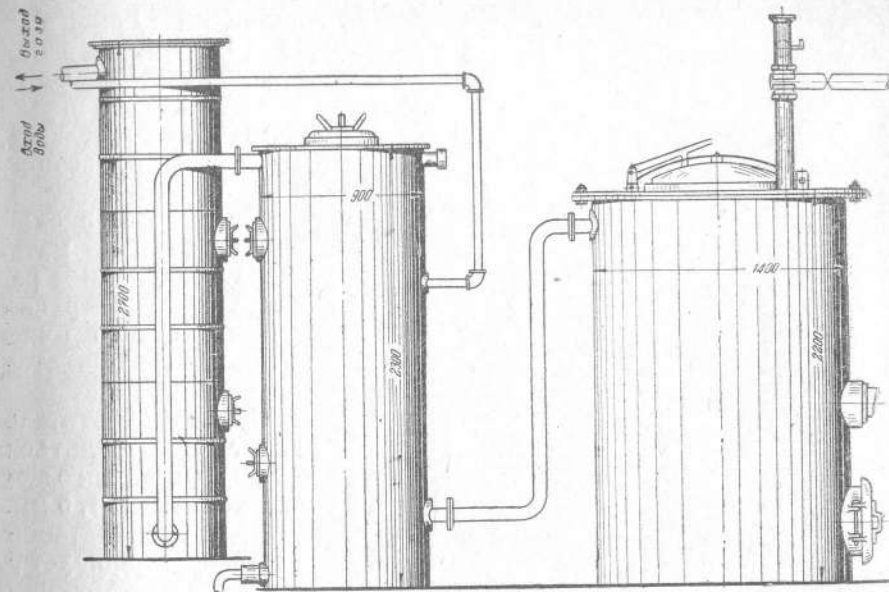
Схема газогенераторной установки конструкции инж. Дубовского
